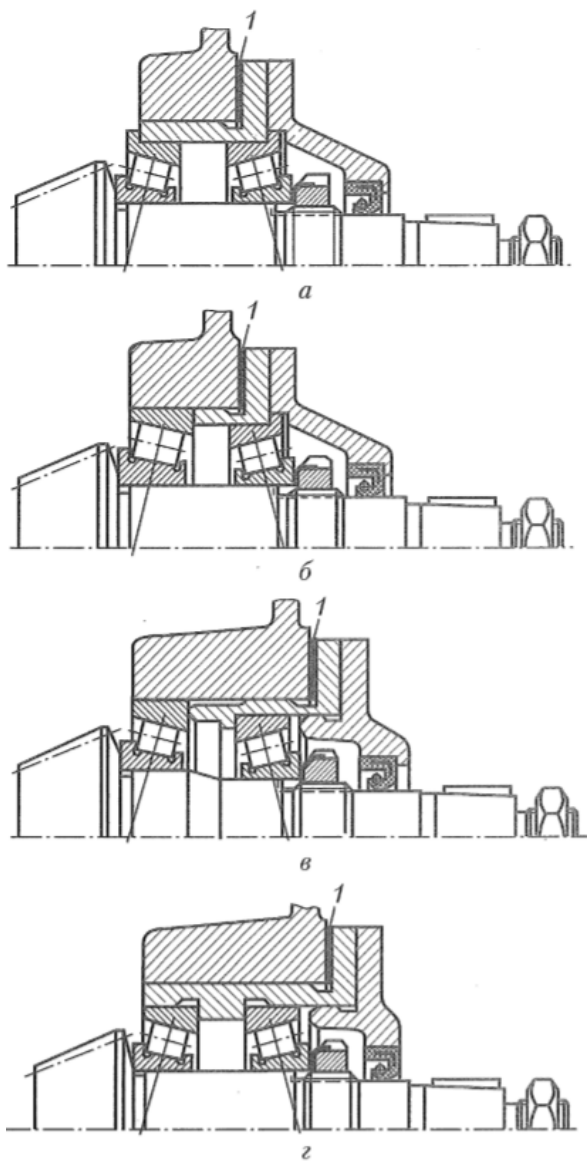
Примеры постановки вала конической шестерни по схеме «встряжку»
